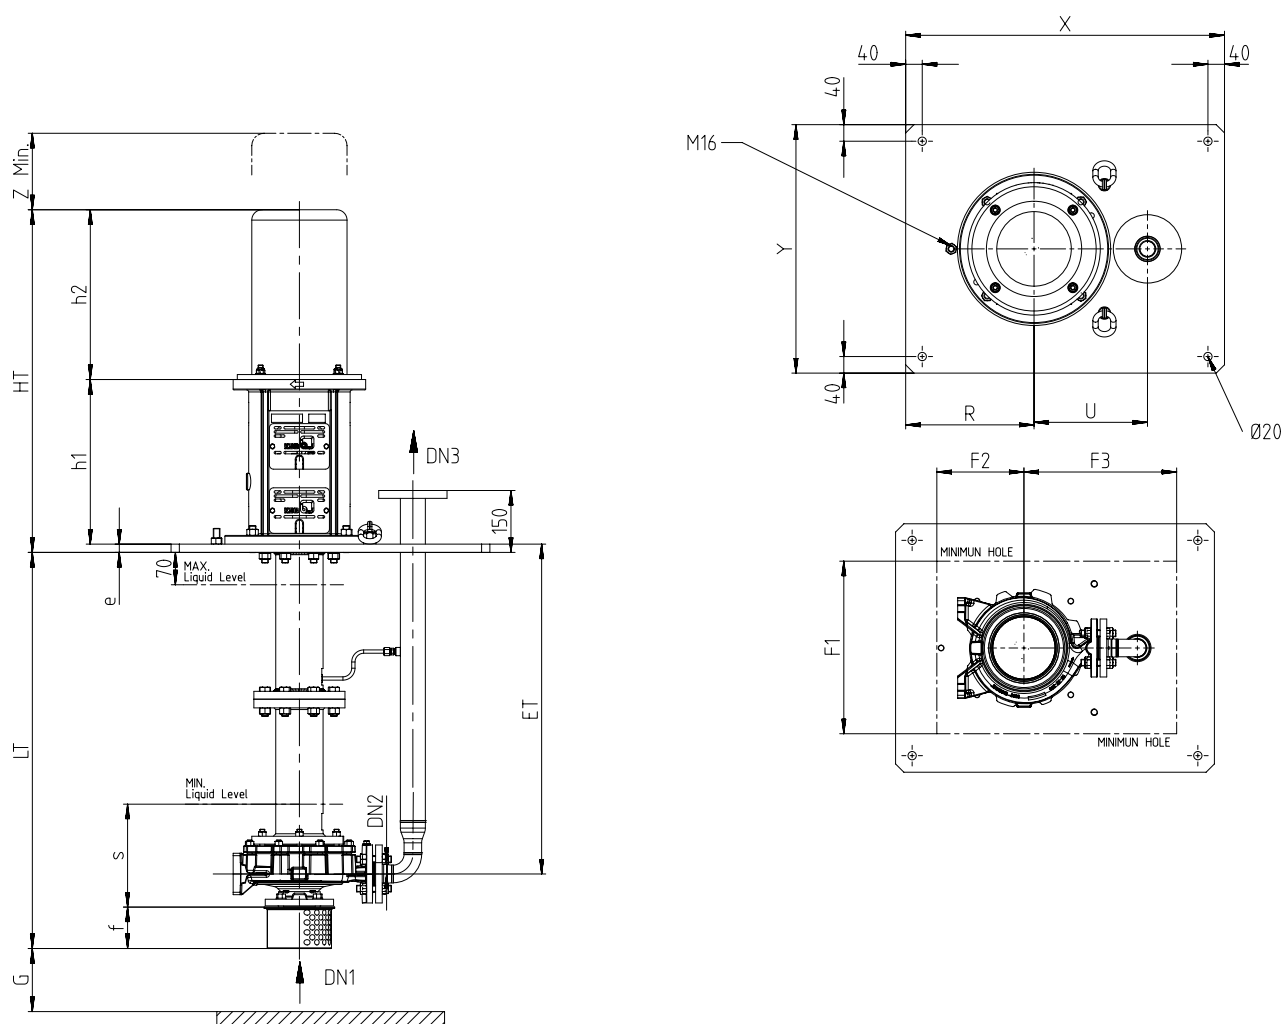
Dimensões da bomba e profundidades de submersão, base rectangular
